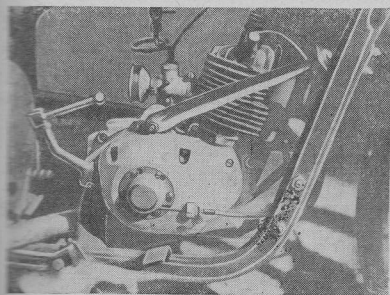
Вид двигателя и коробки передач со стороны сцепления
